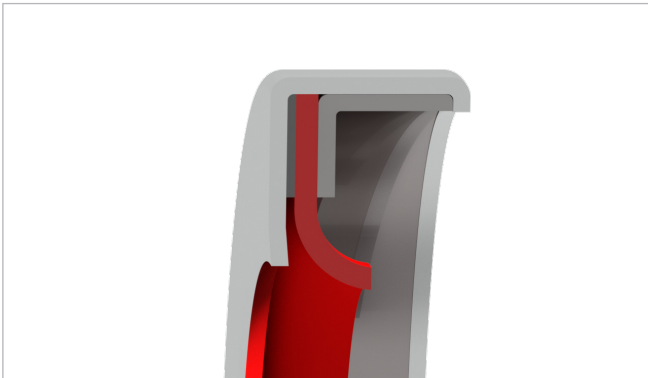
RWD Bauform RR, Ausführung 0, mit einer Dichtlippe. Alternative zu Elastomer RWD Typen
